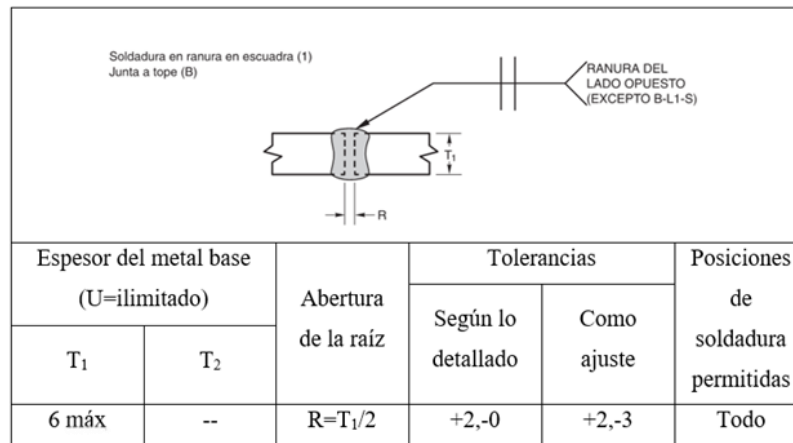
52: Detalles de la junta a tope precalificada en milímetros
